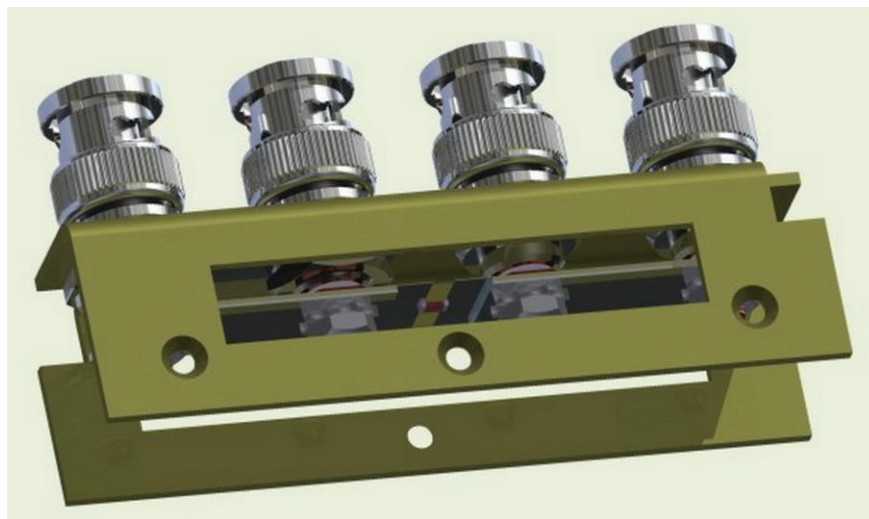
Мера со снятым корпусом. Внешний вид
